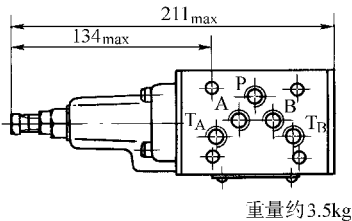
MBP-01、MBA-01、MBB-01 型溢流阀的外形尺寸
